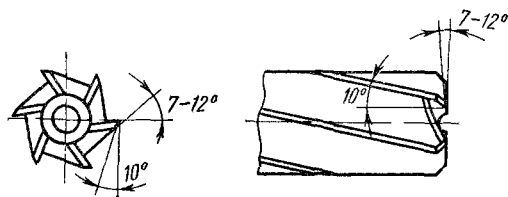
Зенкер для зенкерования отверстий в магниевых сплавах
